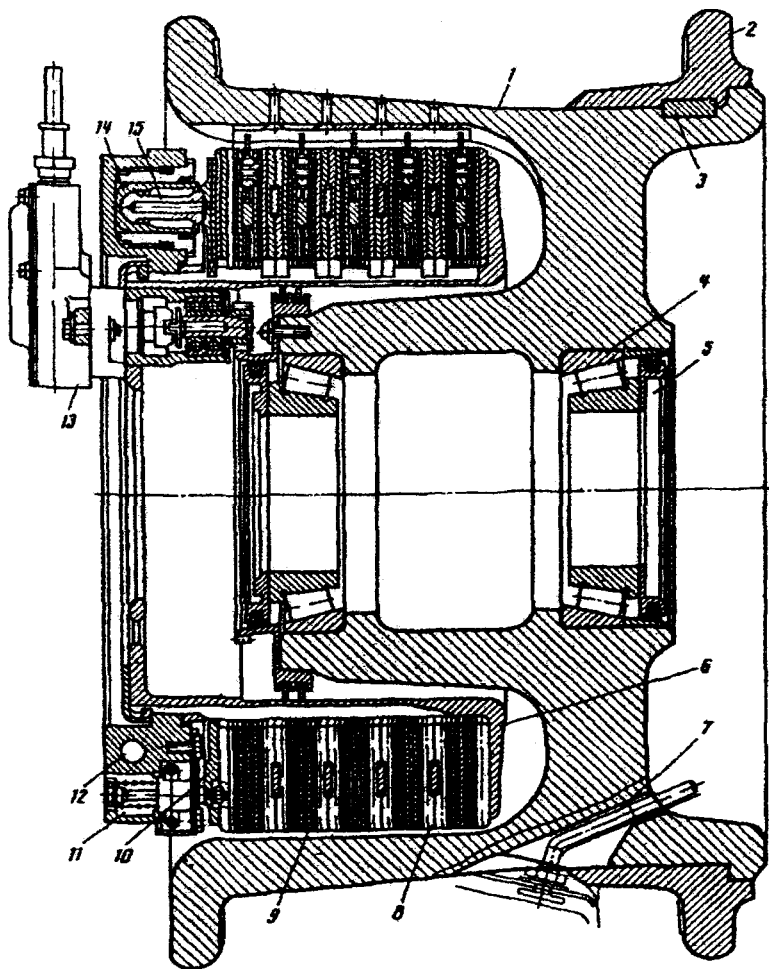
Колесо с дисковым тормозом: 1 – барабан; 2 – съёмная реборда; 3 – шпонка; 4 – роликовый подшипник; 5 – обтюратор; 6 – корпус тормоза; 7 – вентиль; 8,9 – неврвращающийся и вращающийся диски тормозного пакета; 10 – прижимной диск; 11 – пружина растормаживания; 12 – блок тормозных цилиндров; 13 – датчик автомата тормозов (юза); 14 – цилиндр; 15 – поршень
